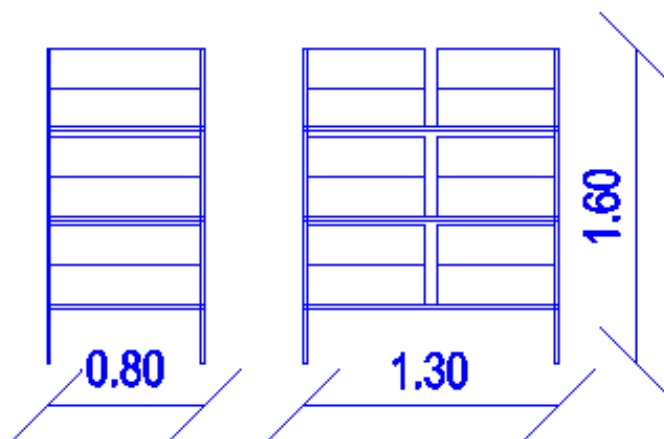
Vista lateral e frontal da rack supermercado standard menor
